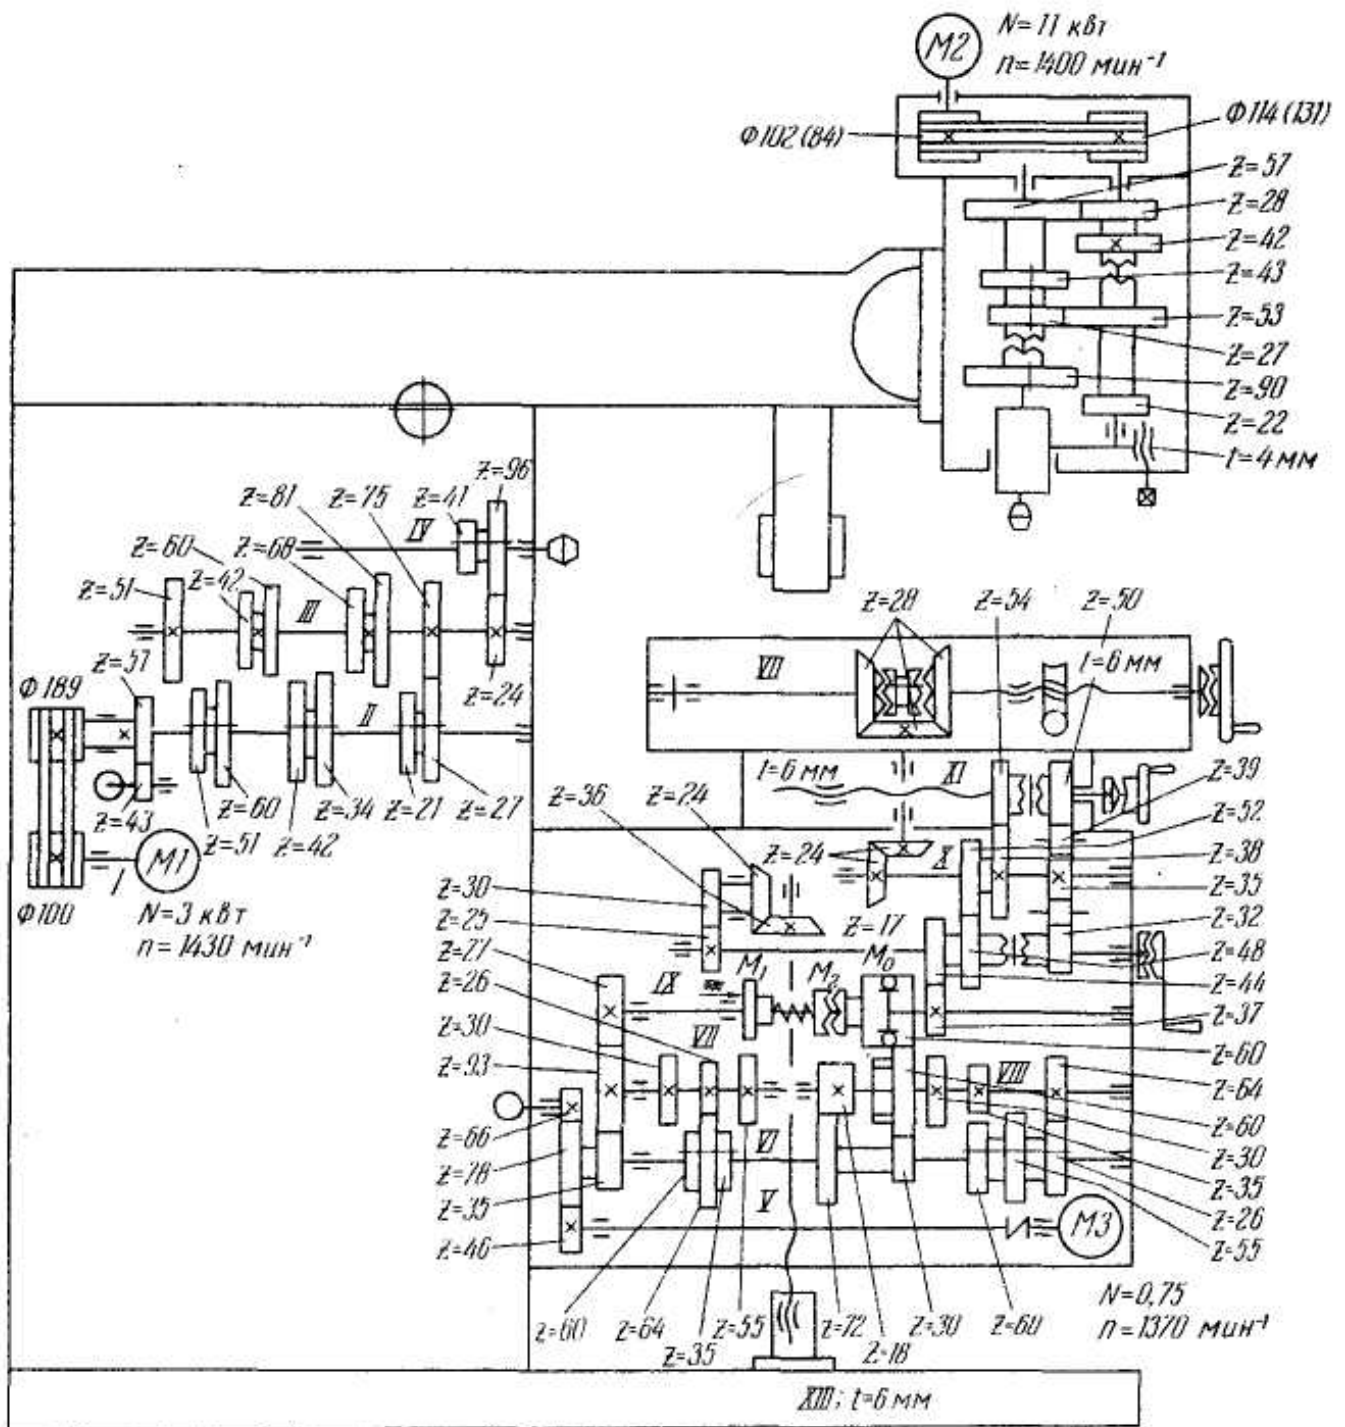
Кинематическая схема станка мод. 6Т80Ш
